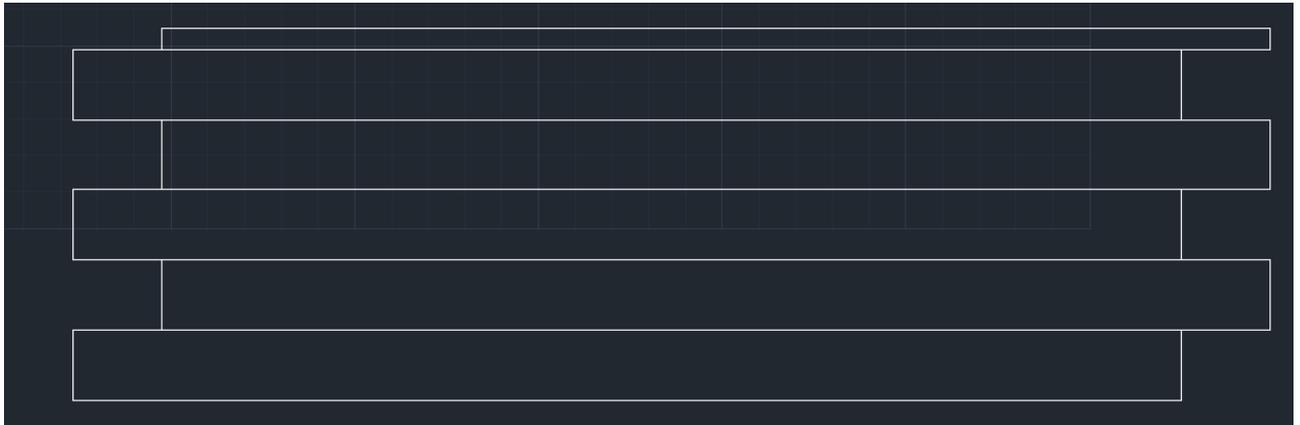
Mapa de soldadura del casco del tanque (con la mejora)
